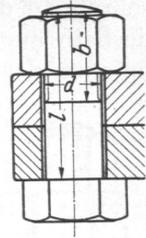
Schraube mit Mutter oder Durchsteckschraube.
